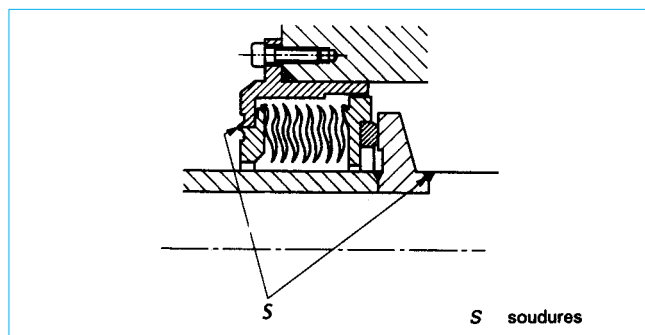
Garniture mécanique à soufflet soudé
